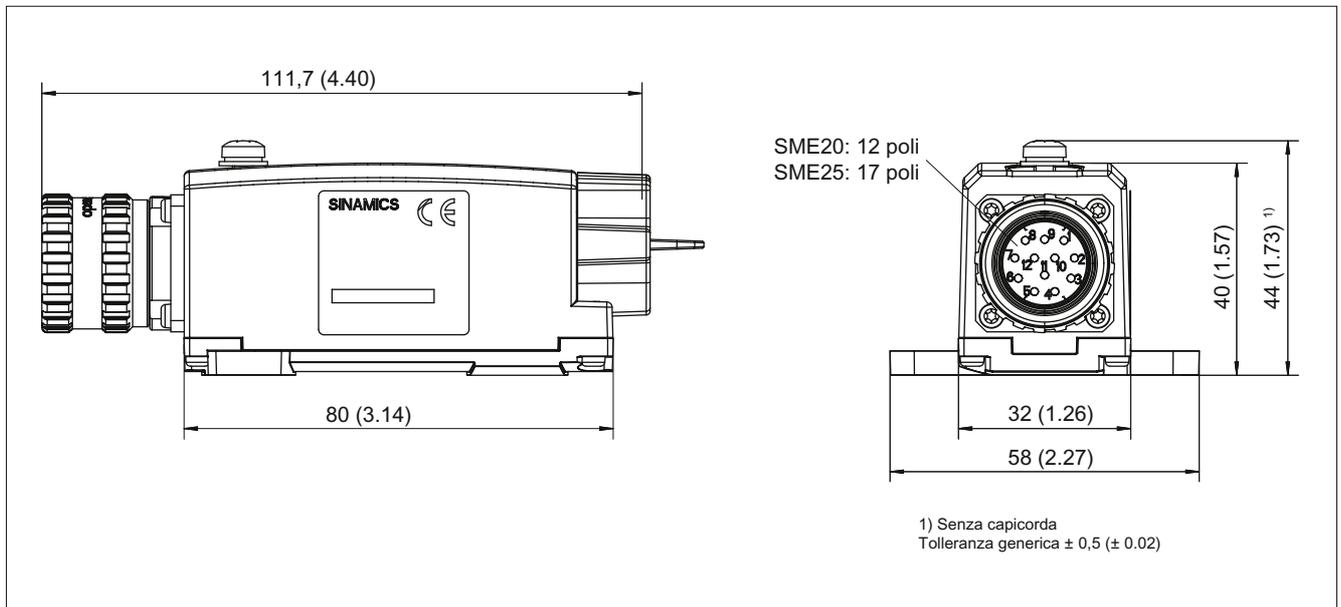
Disegno quotato Sensor Module External SME20, tutte le misure in mm e (inch),
